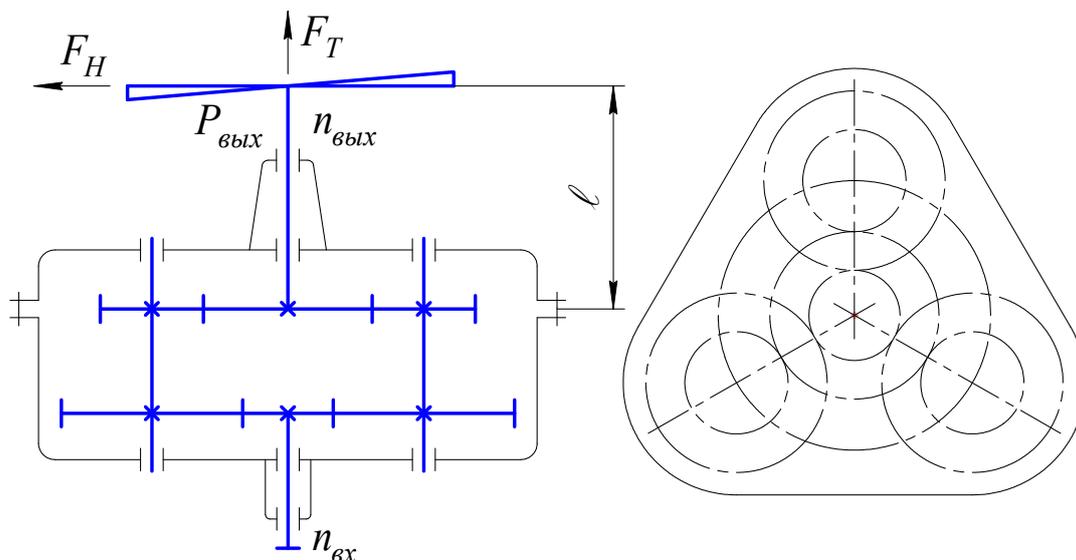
Схема соосного многопоточного цилиндрического редуктора
